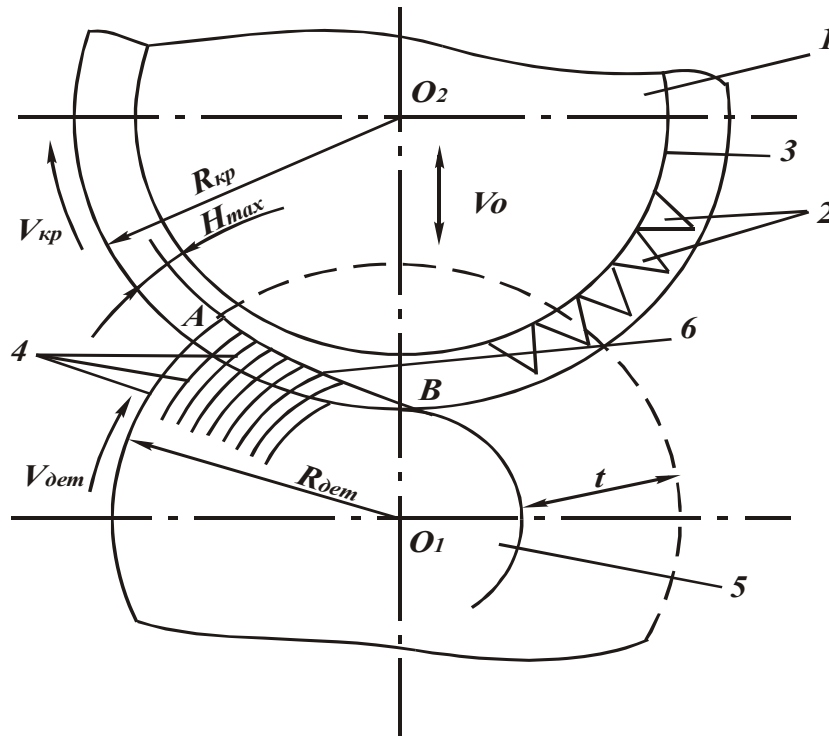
Расчетная схема процесса шлифования: 1 – круг; 2 – зерна; 3 – линия, определяющая положение условной поверхности резания; 4 – цилиндрические оболочки, которыми представлен снимаемый припуск; 5 – заготовка.
